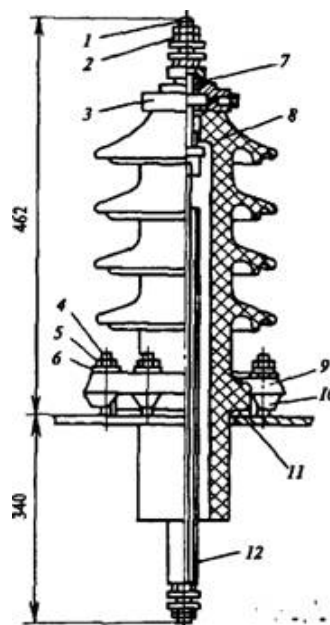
Ввод для наружной установки на напряжение 10 кВ при токе до 250 А с токоведущей шпилькой, присоединяемой к отводу: 1 — медная шпилька; 2 — латунная гайка; 3 — латунный колпак; 4, 5 к 6 — стальные шпилька, гайка, шайба; 7 — резиновое кольцо; 8 — фарфоровый изолятор; 9 — стальной штампованный фланец; 10 — кулачок; 11 — резиновое уплотнение; 12 — токоведущая шпилька с изолирующей трубкой
